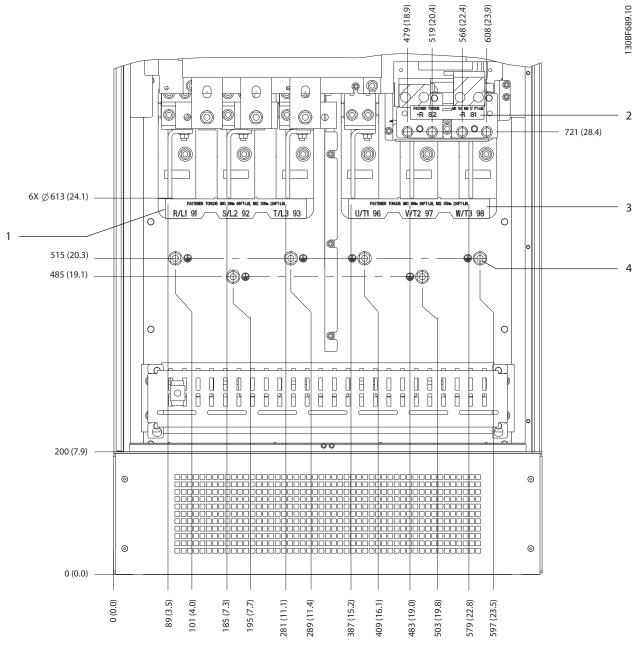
Dimensions des bornes E1h (vues latérales)
